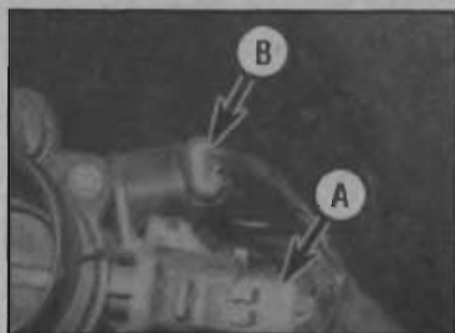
Расположение разъема потенциометра положения дроссельной заслонки (А) и шагового двигателя (В) — поздний двигатель 1,6 л
